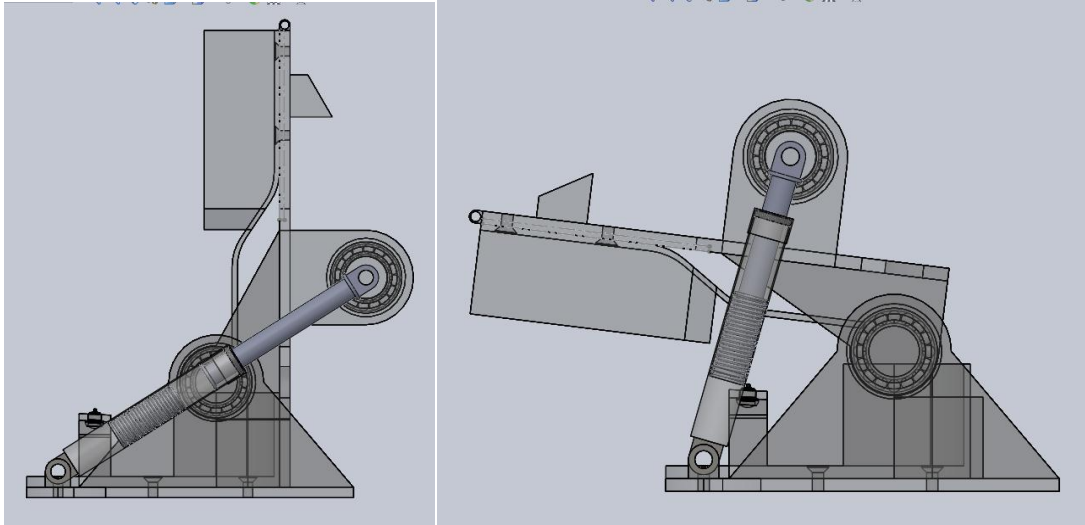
Ensamble del elemento de soporte con elementos de canilla y pie
